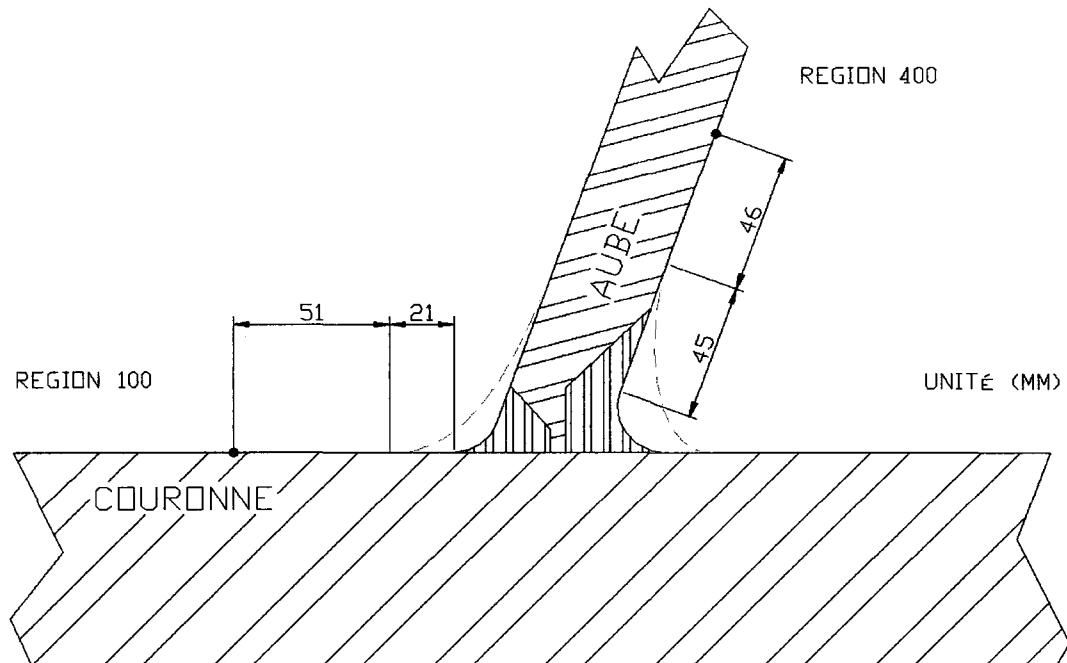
Position des jauges percées pour les mesures après soudage
